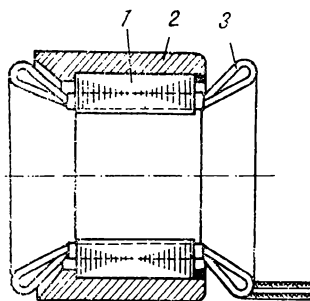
Pachetul statoric fixat în carcasă de aluminiu: 1 — pachet statoric; 2 — carcasă de aluminiu; 3 — capetele de bobine.
